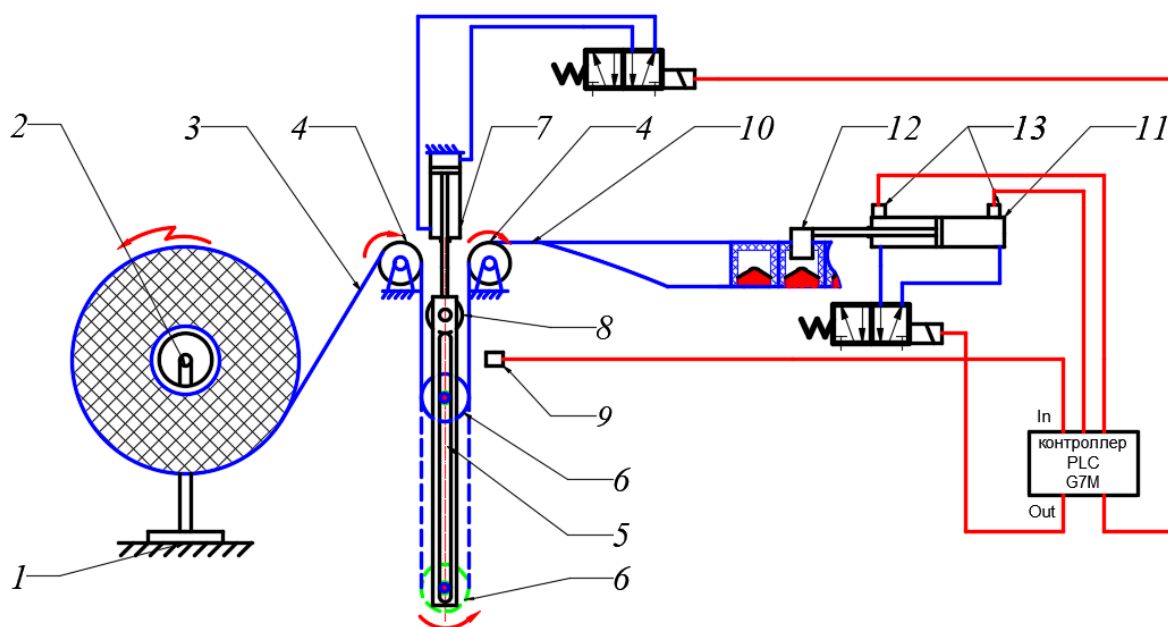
Схема устройства разматывания и протягивания упаковочного материала: 1 – узел установки рулона; 2 – рулон; 3 – упаковочный материал; 4 – отклоняющие ролики; 5 – прорези; 6 – натяжной ролик; 7 – цилиндр разматывания рулона; 8 – толкающие ролики; 9, 13 – датчики положения; 10 – формователь пакетов; 11 – цилиндр протягивания; 12 – захват
